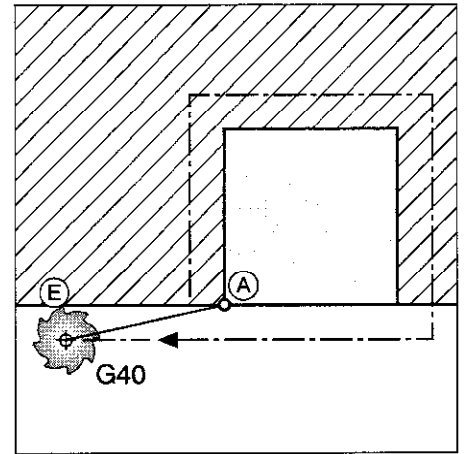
Endpunkt (E) einer Bearbeitung
